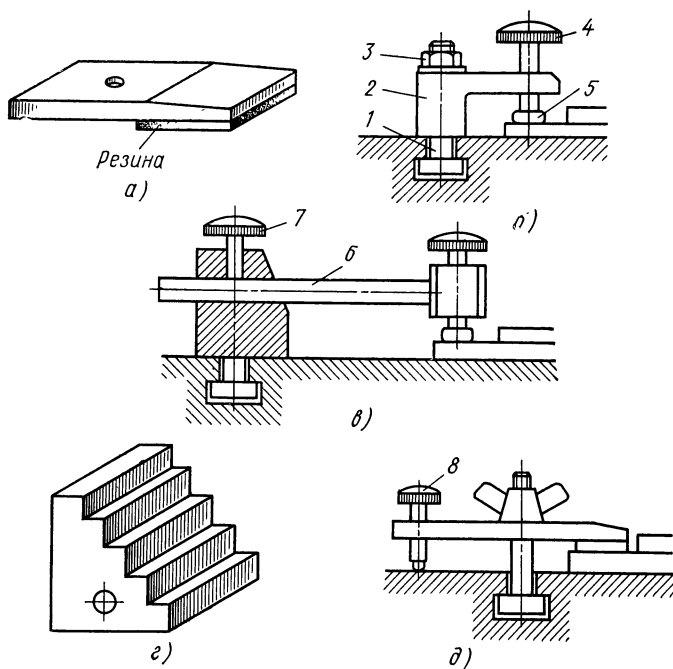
Оснастка для крепления на станках стеклянных подкладок:
